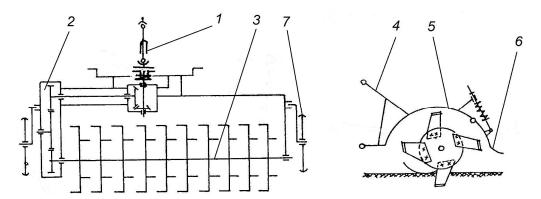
Schema frezei cu rotor orizontal: 1- transmisie cardanică; 2- transmisie mecanică; 3-rotor cu cuțite; 4- triunghi prindere la tractor; 5- carcasă; 6- capac mobil; 7- roți de sprijin
